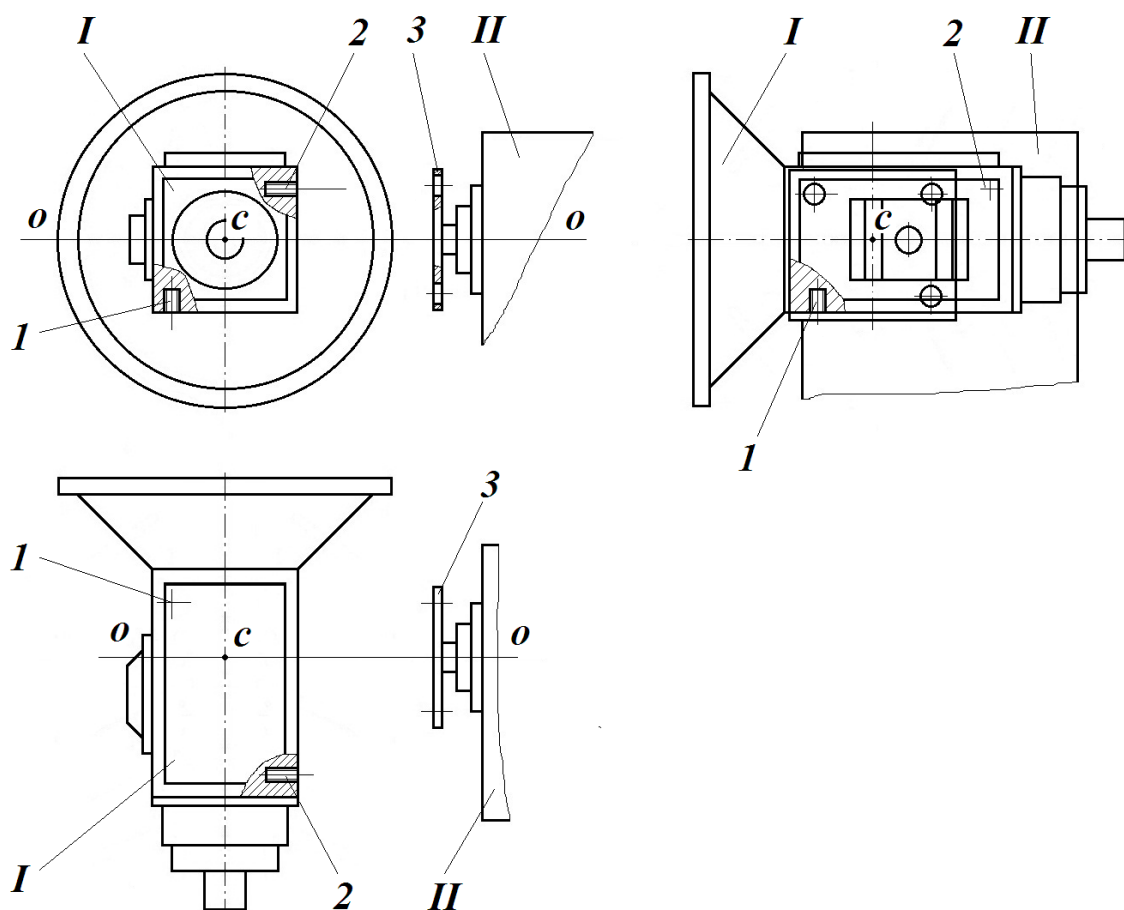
Конструктивные элементы корпусной детали агрегата, используемые для закрепления на адаптере разборочно-сборочного стенда
